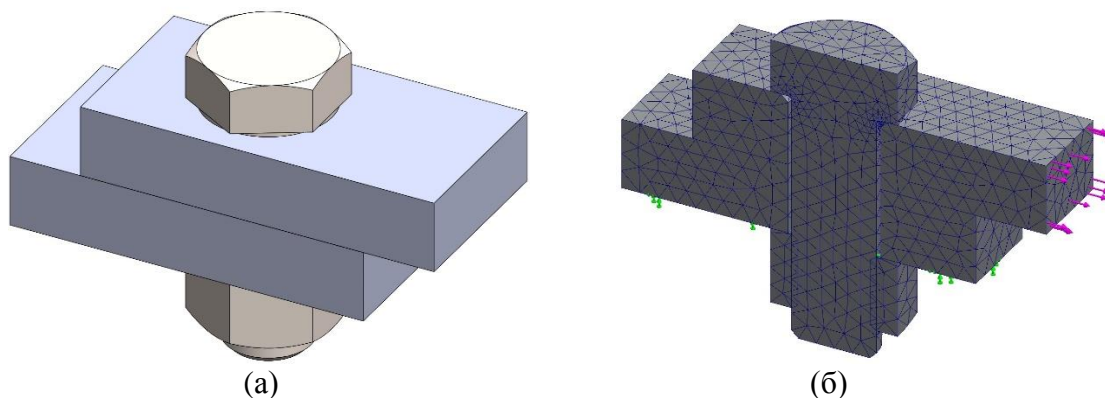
Твердотільна (а) та кінцевоелементна (б) модель різьбового з'єднання
